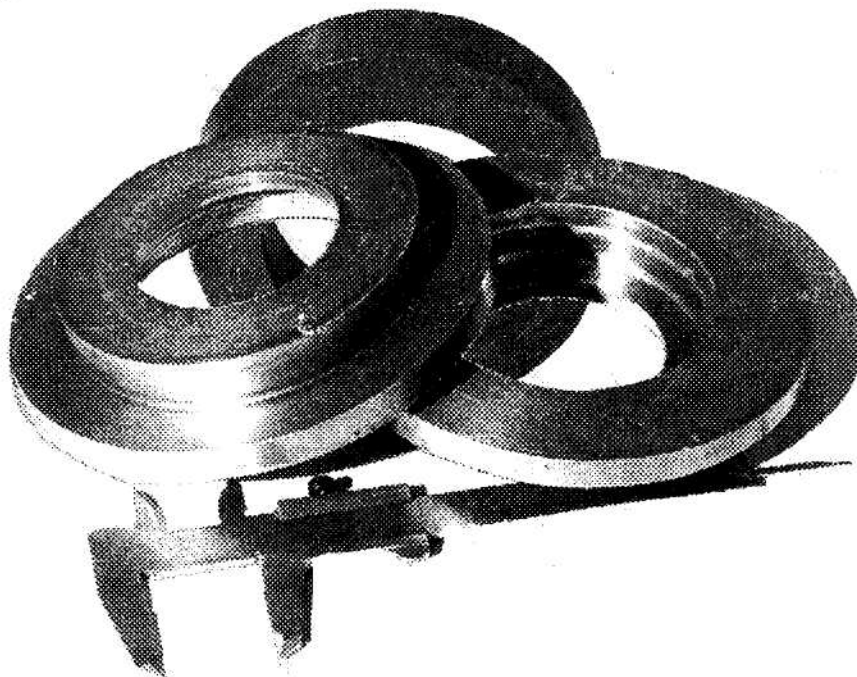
Заготовка і відштамповані обкочуванням катки ходової системи гусеничного трактора
